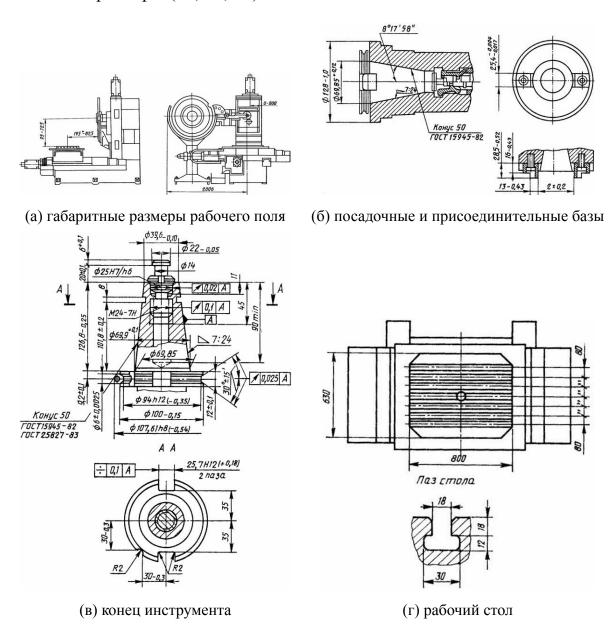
Посадочные и присоединительные размеры станка 2206ВМФ4
